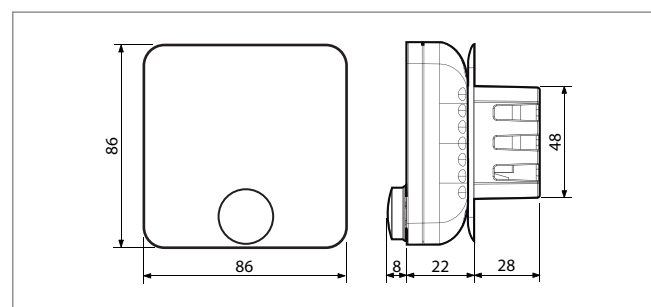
Maßblatt für das Zonen-Bediengerät für Unterputzmontage (Maße in mm)
